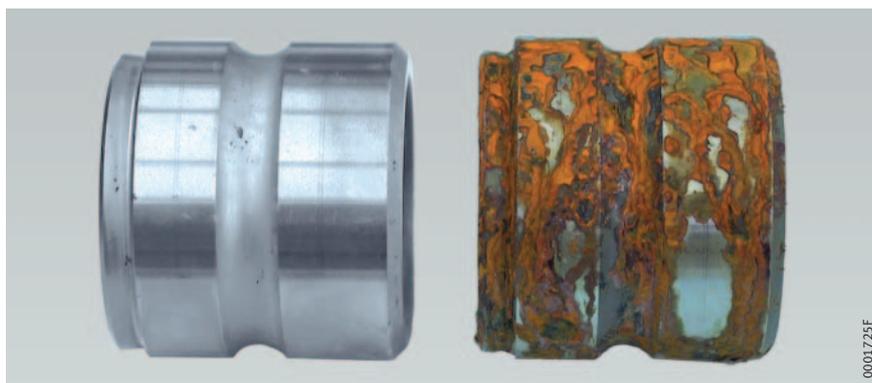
· Mit und ohne Beschichtung im Salzsprühtest
